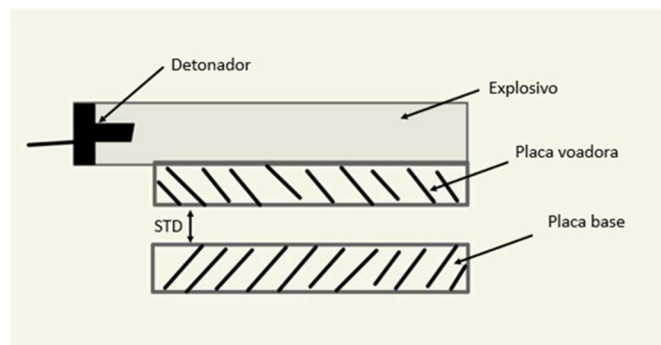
Configuração paralela do processo de soldadura por explosão.
